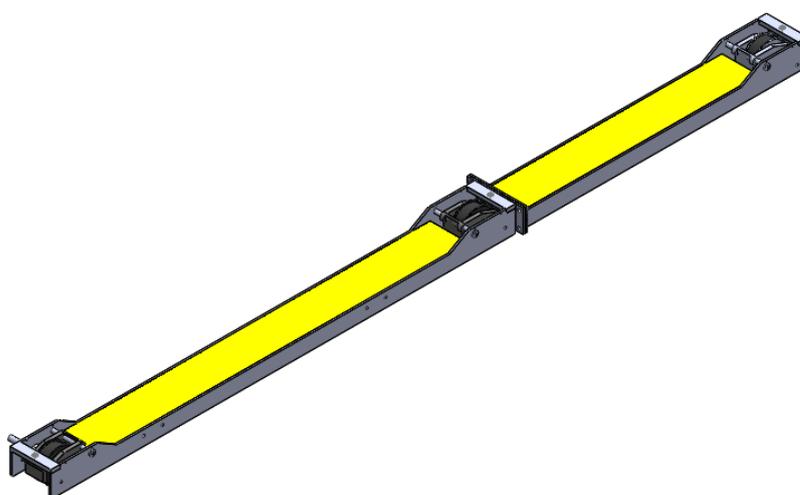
Gruppo Ruota e Motoriduttore per caricatrice
